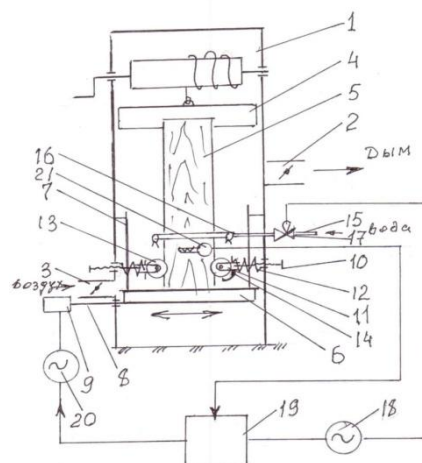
Функциональная схема устройства для генерации дыма с рабочим органом в виде виброплощадки: 1 – корпус; 2 – патрубок подачи дыма; 3 – патрубок подачи воздуха; 4 – прижимное приспособление; 5 – материал тления (брусок); 6 – пластина; 7 – тяги (подвесы); 8 – штанга – толкатель; 9 – вибратор электромагнитный; 10 – винтовая пара; 11 – трубка телескопической пары; 12 – пружина; 13 – ролик; 14 – тормозной элемент с биметаллической пластиной; 15 – трубопровод подачи воды; 16 – форсунка; 17 – кран; 18-20 – исполнительные механизмы переменного тока; 19 – блок управления; 21 – датчик температуры
